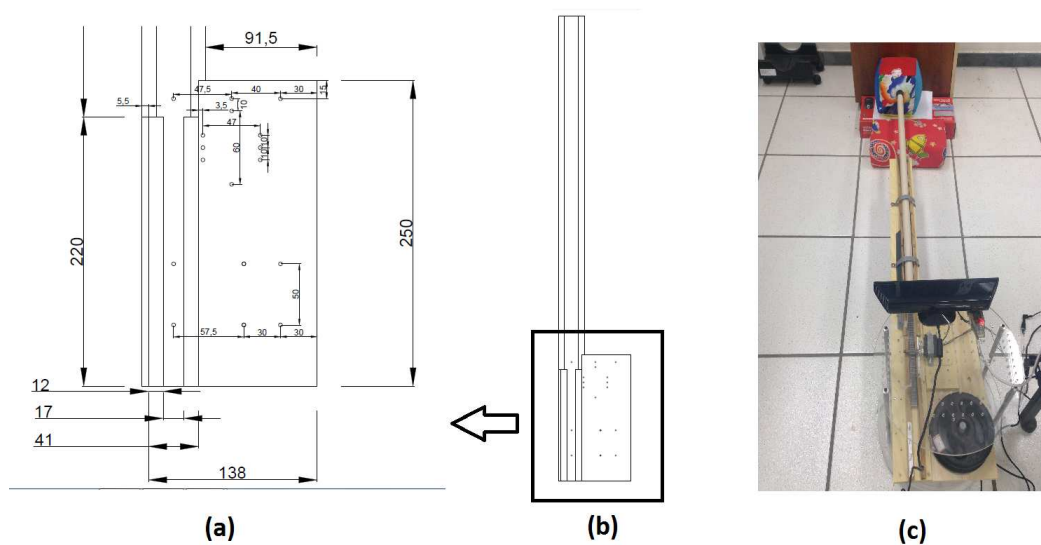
Atuador Linear - (a) Projeto preliminar - Dimensões. (b) Projeto preliminar - Visão de conjunto. (c) Construção final. Dimensões em mm.
